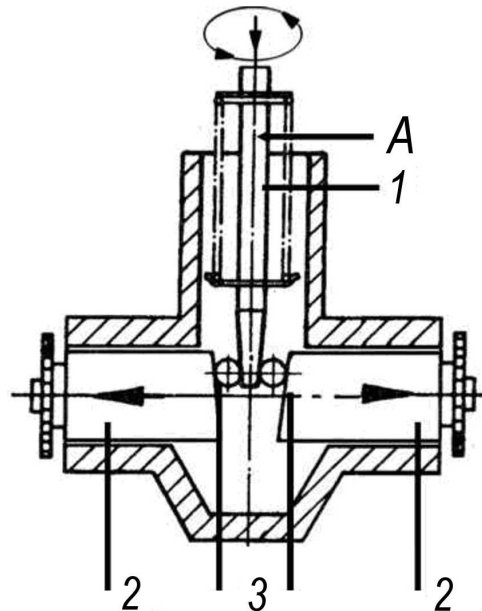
Регулировка автоматическая распорно-клинового механизма
